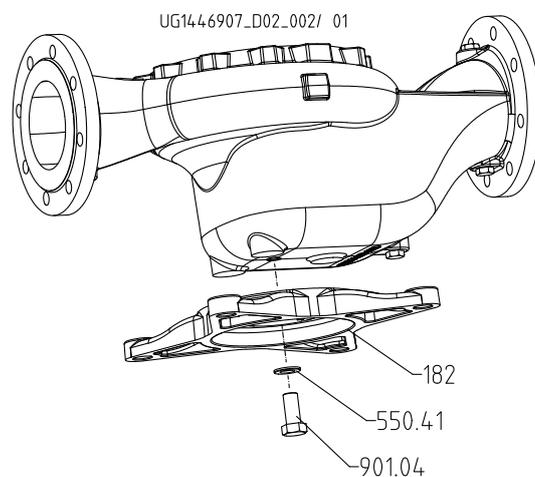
Vertikalaufstellung mit Pumpenfuß
